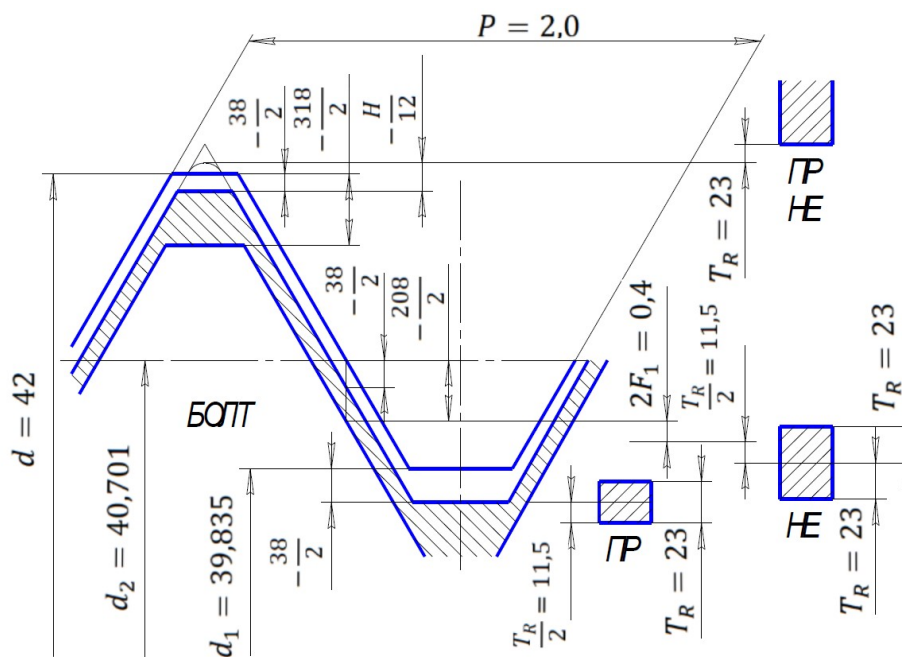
Схема розташування полів допусків зовнішньої різьби і калібрів-кілець ПР і НЕ
